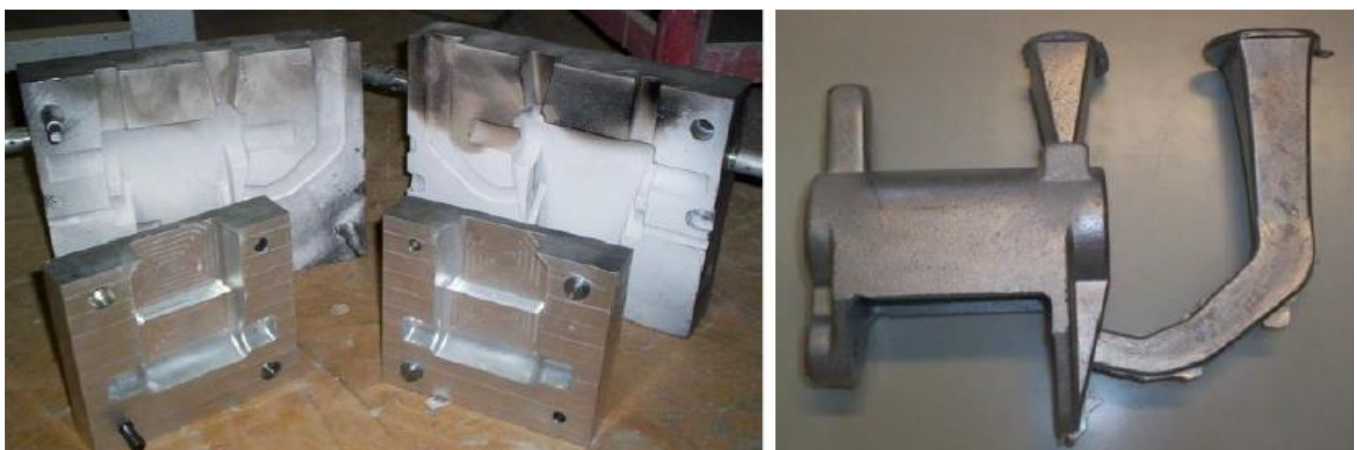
Moule en coquille et boîte à noyau ouverts, et la pièce obtenue brute de moulage.
